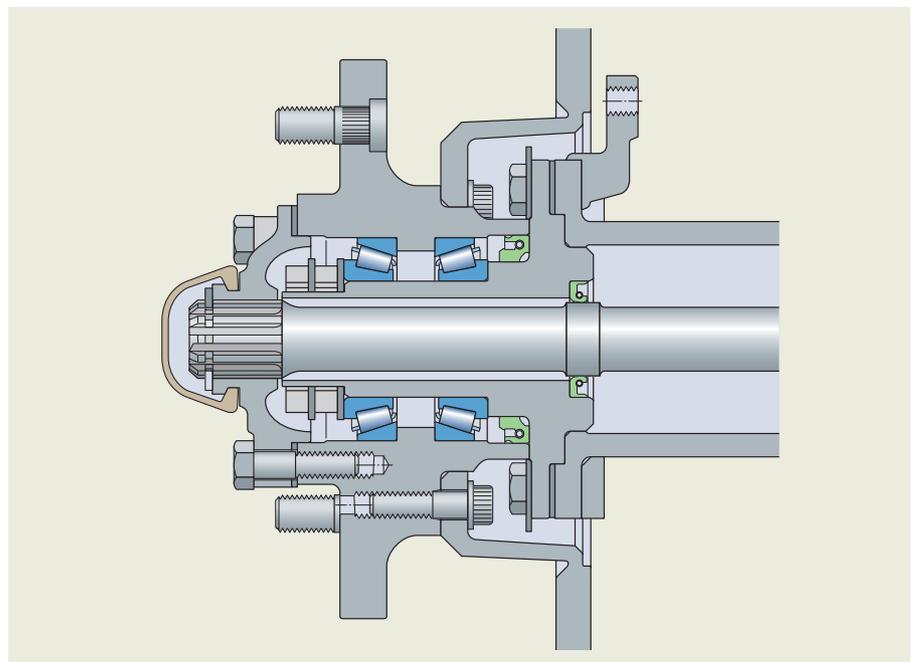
Disposición de rodamientos en un cubo de rueda de tracción trasera
